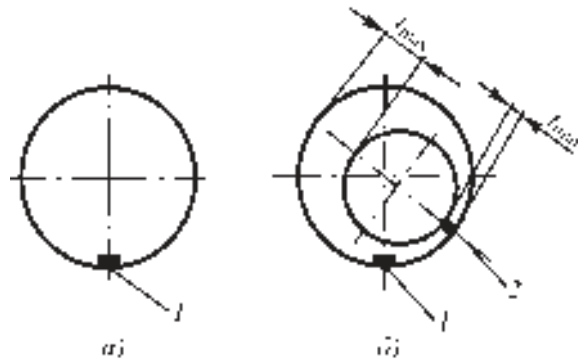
Настройка центрирующего узла штампа по насечкам на заготовке (а) и изделии (б)
